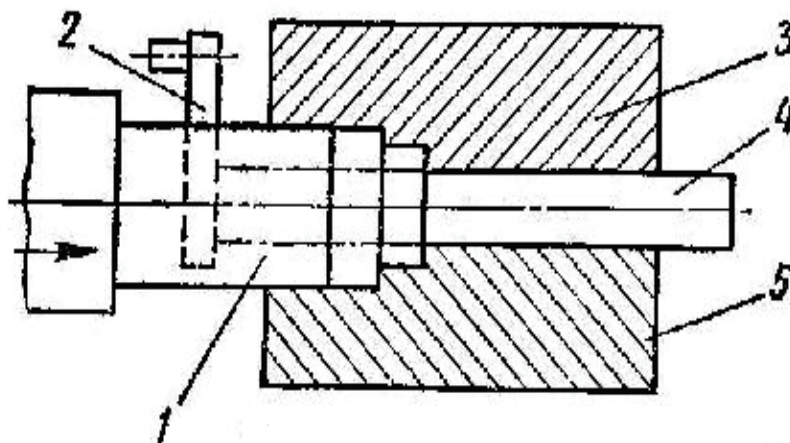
Схема штамповки ступенчатого вала с фланцем на ГКМ
